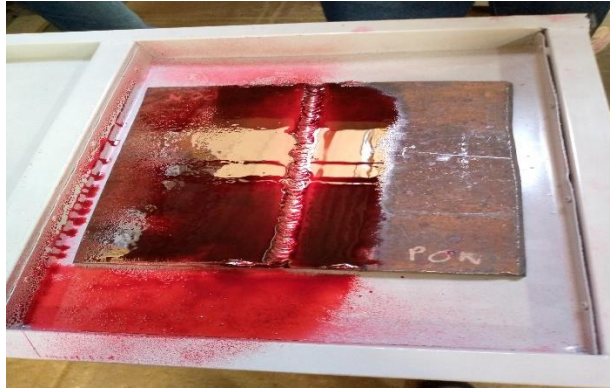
Líquido penetrante visible de color rojo, aplicado en probeta de soldadura.
